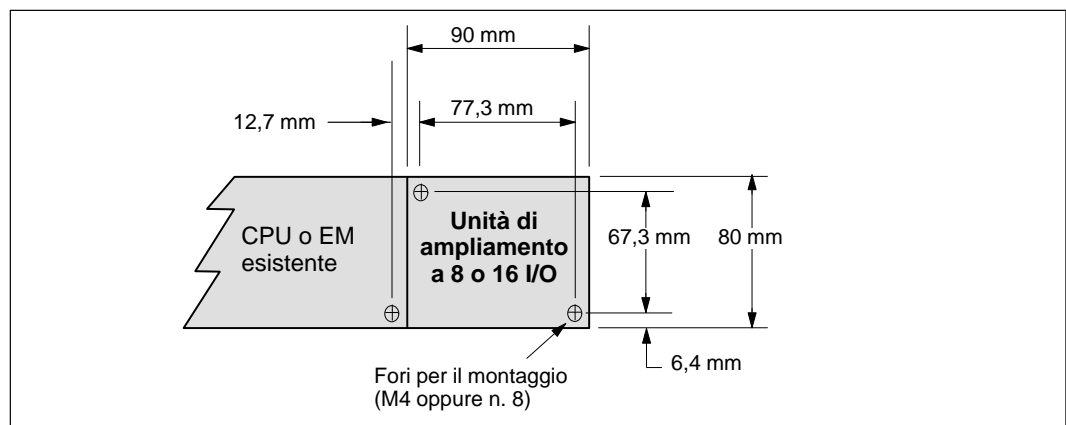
Dimensioni per il montaggio di una unità di ampliamento a 8 e 16 I/O
